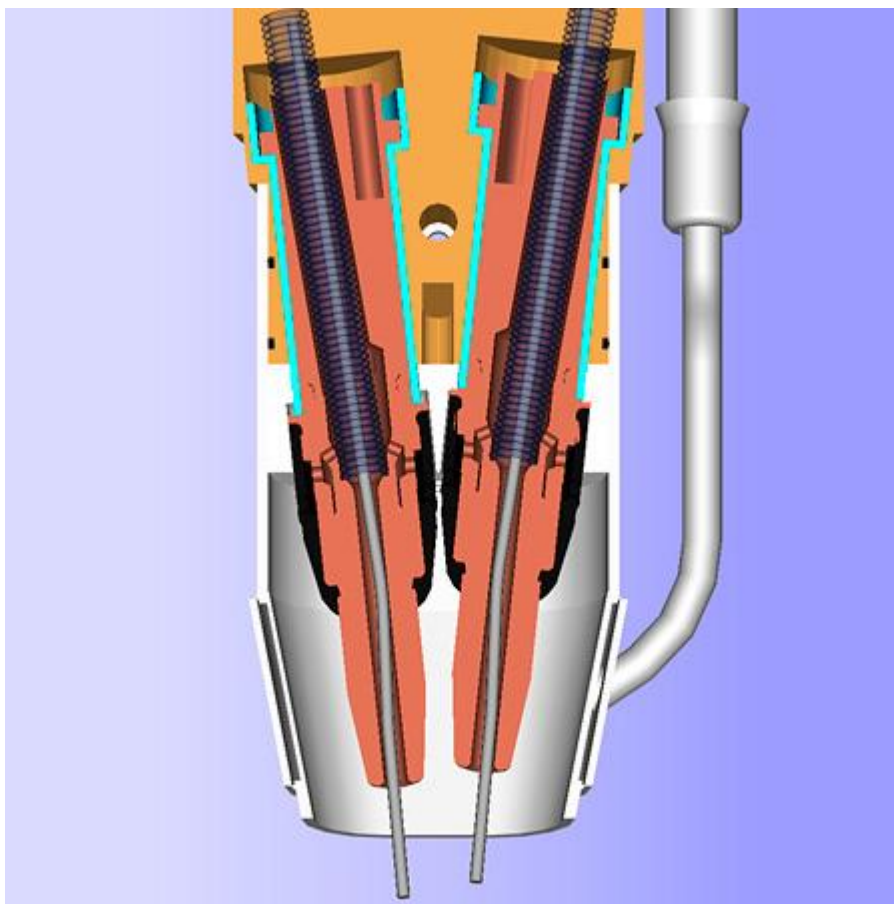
Сварочная горелка для тандемной технологии TimeTwin в разрезе
